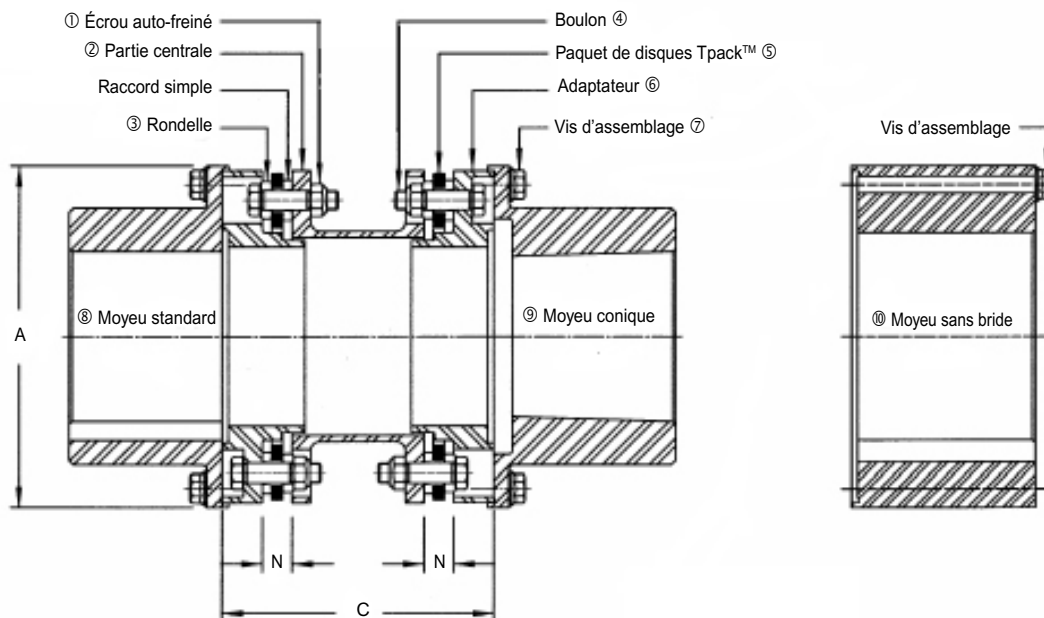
Vue en coupe des composants d'accouplement Thomas de la série 71-8. Cette vue présente les trois types de moyeux disponibles adaptés à des exigences précises. Une configuration standard inclut uniquement deux moyeux.
